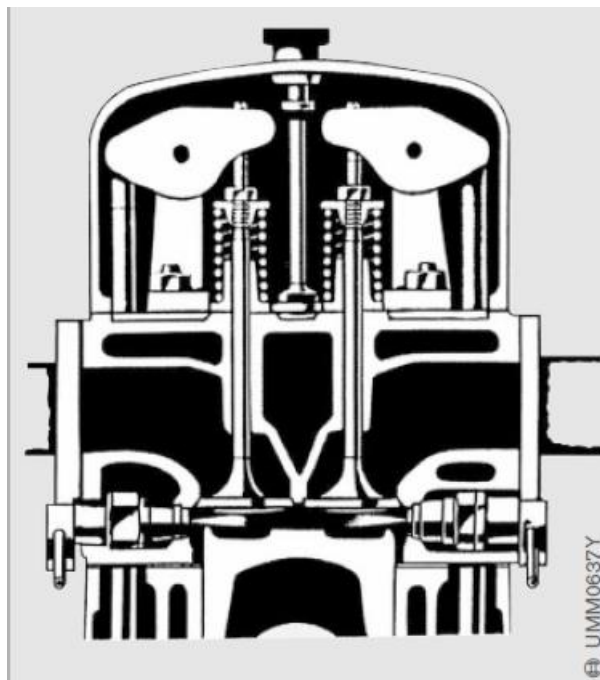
Princíp motoru s predspaľovacou komorou [1]
